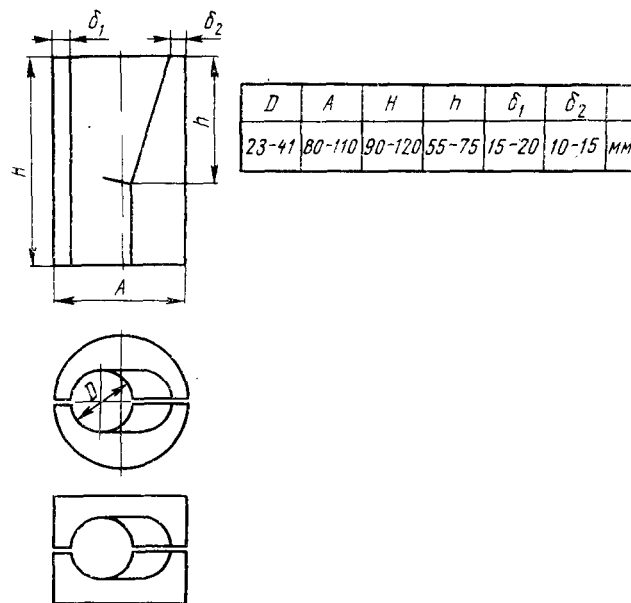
Конструкции инвентарных медных форм для сварки стыковых соединений вертикальных стержней диаметром 20—36 мм
